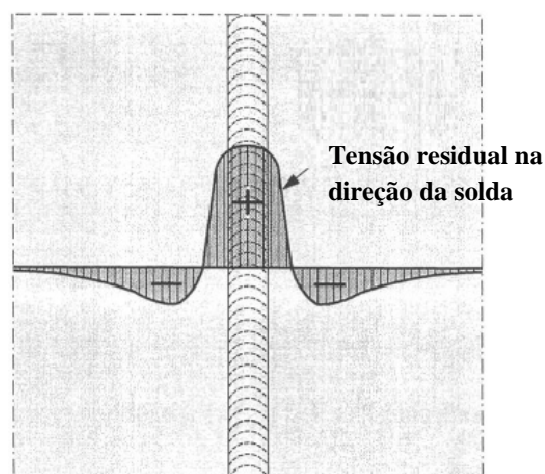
Tensão residual devido ao processo de soldagem
